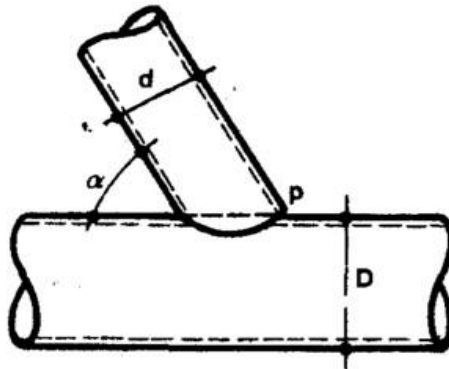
Schéma explicatif de la condition de coupe en forme de tube [8]
